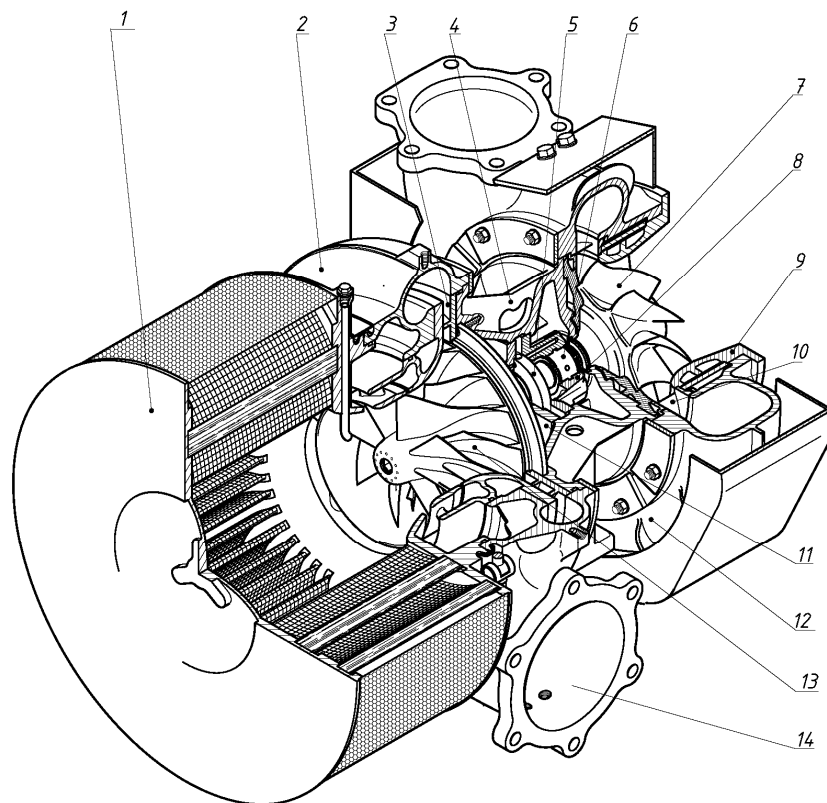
Турбокомпресор з радіальної турбіною типу TPS52-F: 1 – повітряний фільтр; 2 – вихідний патрубок компресора; 3 – дифузор, 4 – корпус підшипникового вузла; 5 – осьовий підшипник; 6 – радіальний підшипник зі сторони турбінного колеса; 7 – турбінне колесо; 8 – підшипниковий вузол; 9 – дефлектор турбіни; 10 – направляючий апарат турбіни; 11 – ущільнення з боку компресора; 12 – вихідний патрубок турбіни; 13 – колесо компресора
